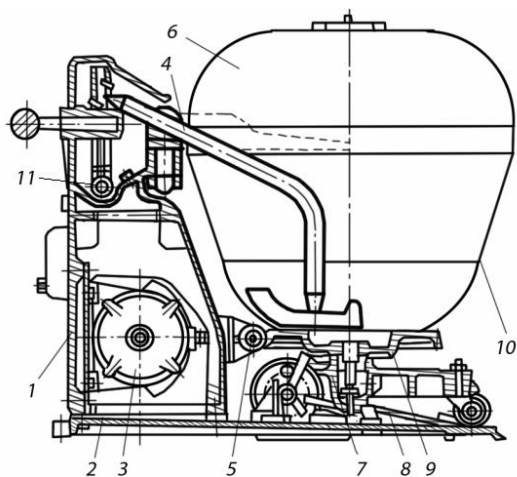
Тістомісильна машина з підкатною діжею: 1 – станина; 2 – фундаментна плита; 3 – електродвигун; 4 – місильний важіль; 5 – черв'як; 6 – кришка; 7 – трьхколісний візок; 8 – фіксатор; 9 – зубчастий вінець, 10 – діжа; 11 – черв'ячний редуктор
